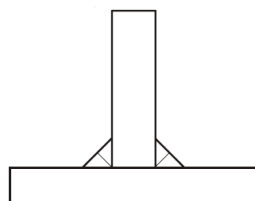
Soldadura de ligação dos banzo com a alma. [34]
